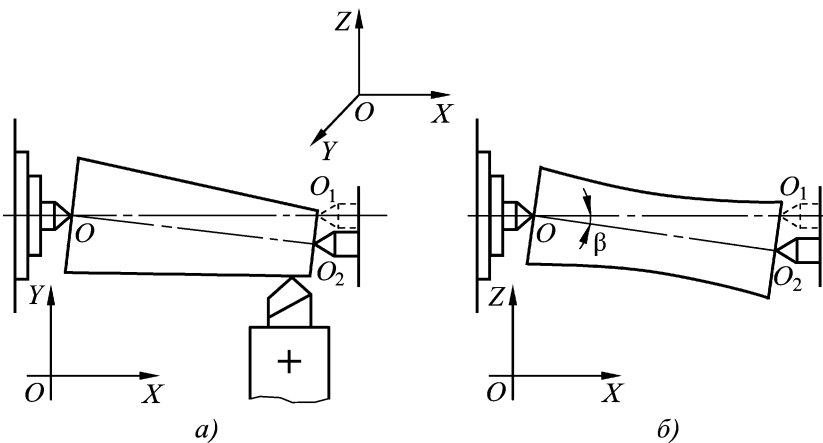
Схема образования геометрической погрешности токарно-винторезного станка:
